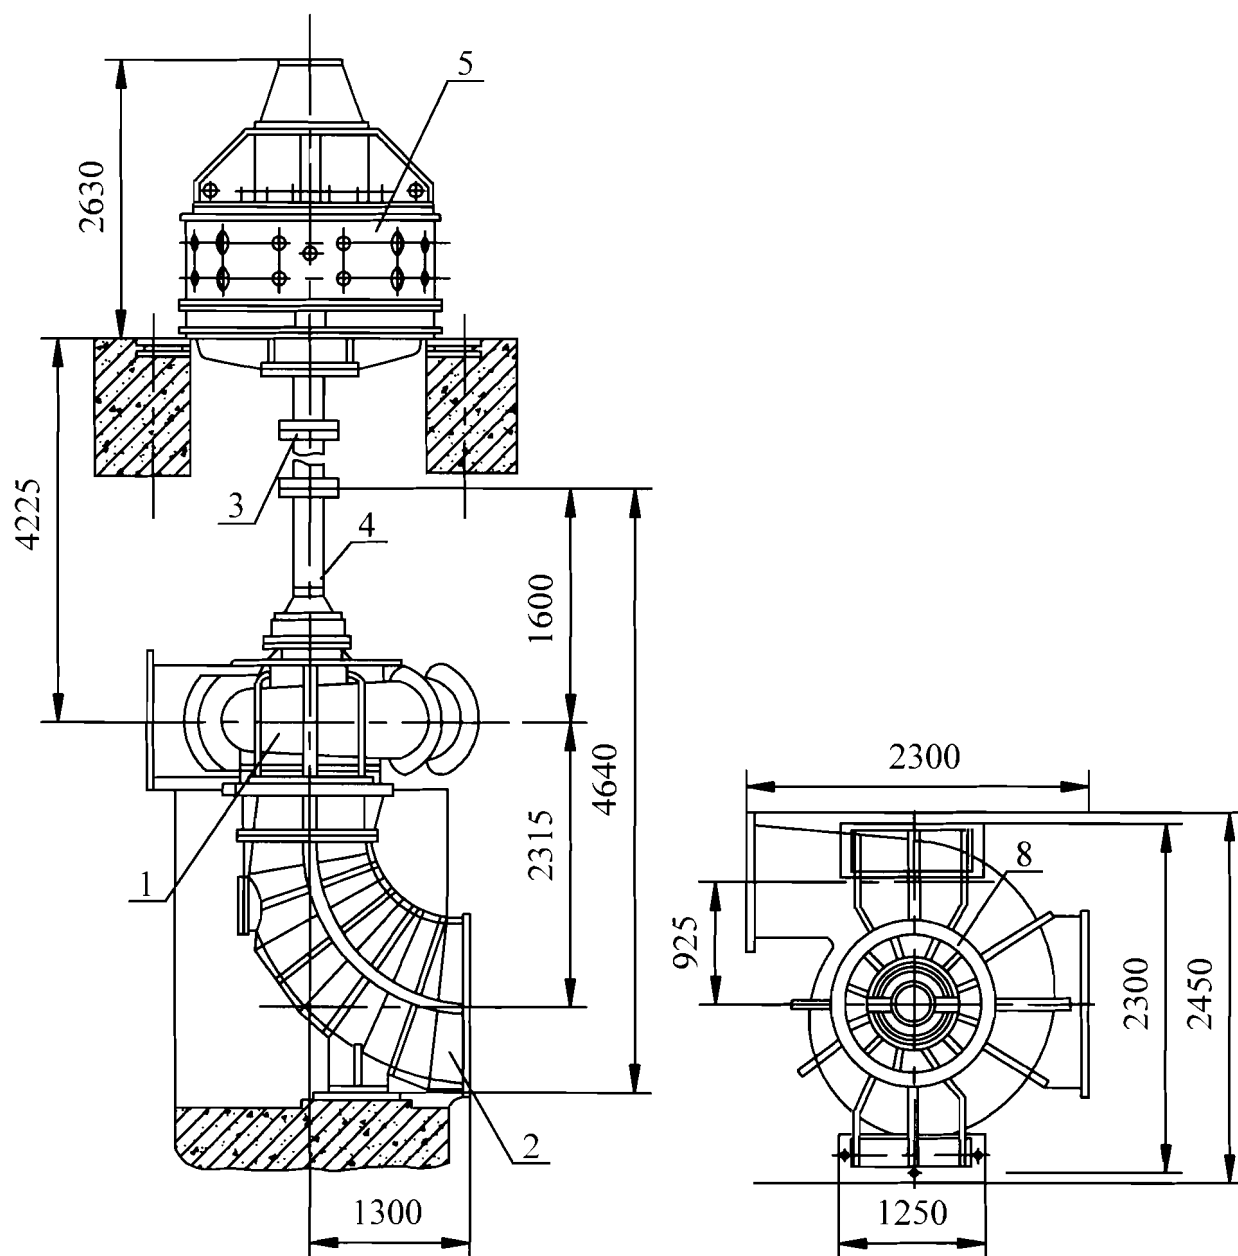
Установочный чертеж НТВ VC20D01(02)
